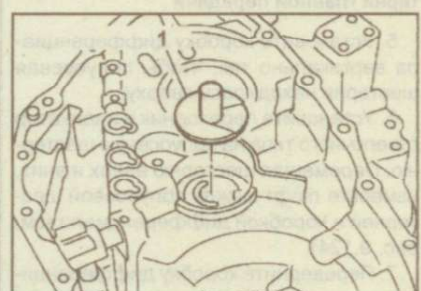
Установка канала (1) для смазки вторичного вала
